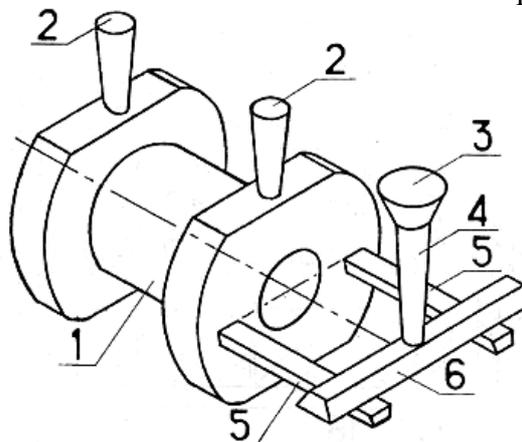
Эскиз отливки с элементами литниковой системы: 1 - отливка; 2 - выпор; 3 - чаша; 4 - стояк; 5 - питатель; 6 - шлакоуловитель
